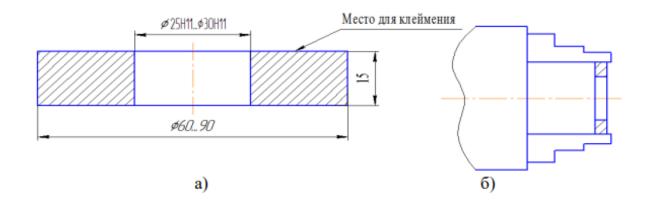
Заготовка (а) и схема закрепления ее в патроне (б)
